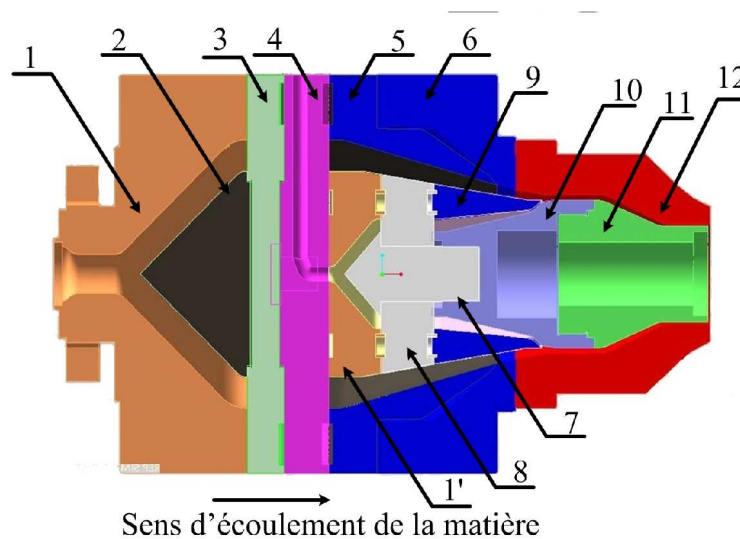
Vue en coupe de la tête d'extrusion.
